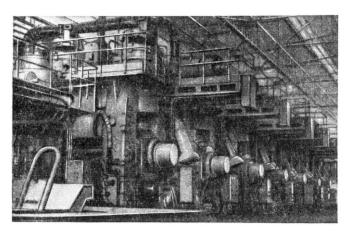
Непрерывный широкополосовой стан горячей прокатки.
